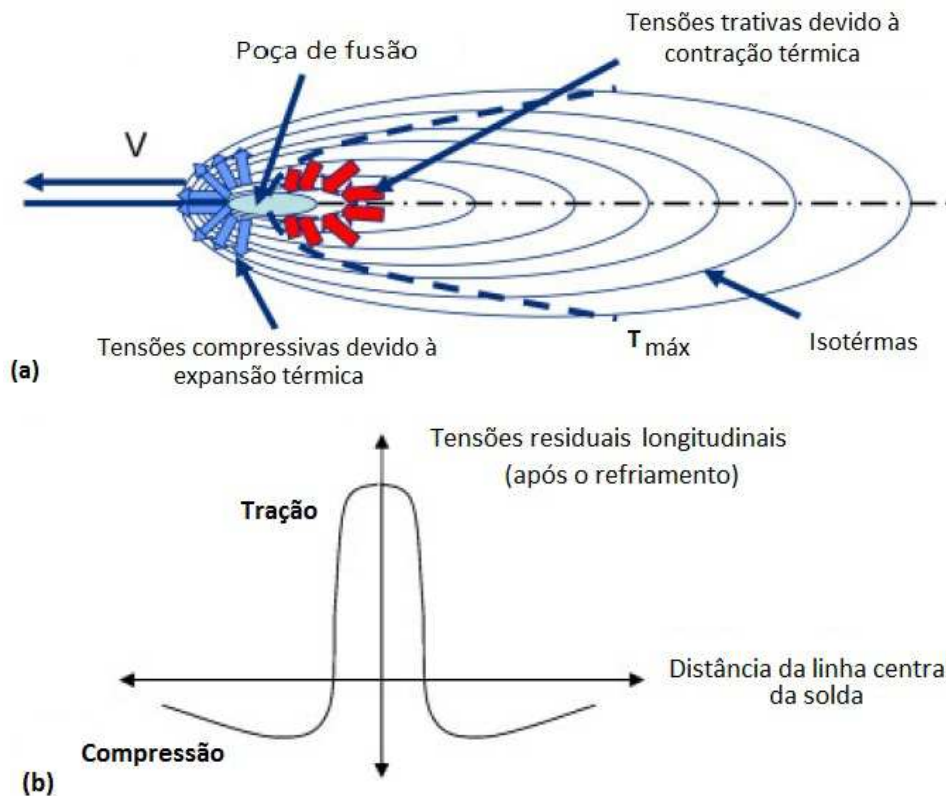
(a) Tensões térmicas durante a soldagem. (b) Tensões residuais longitudinais pós-soldagem (Colegrove et al., 2009).
